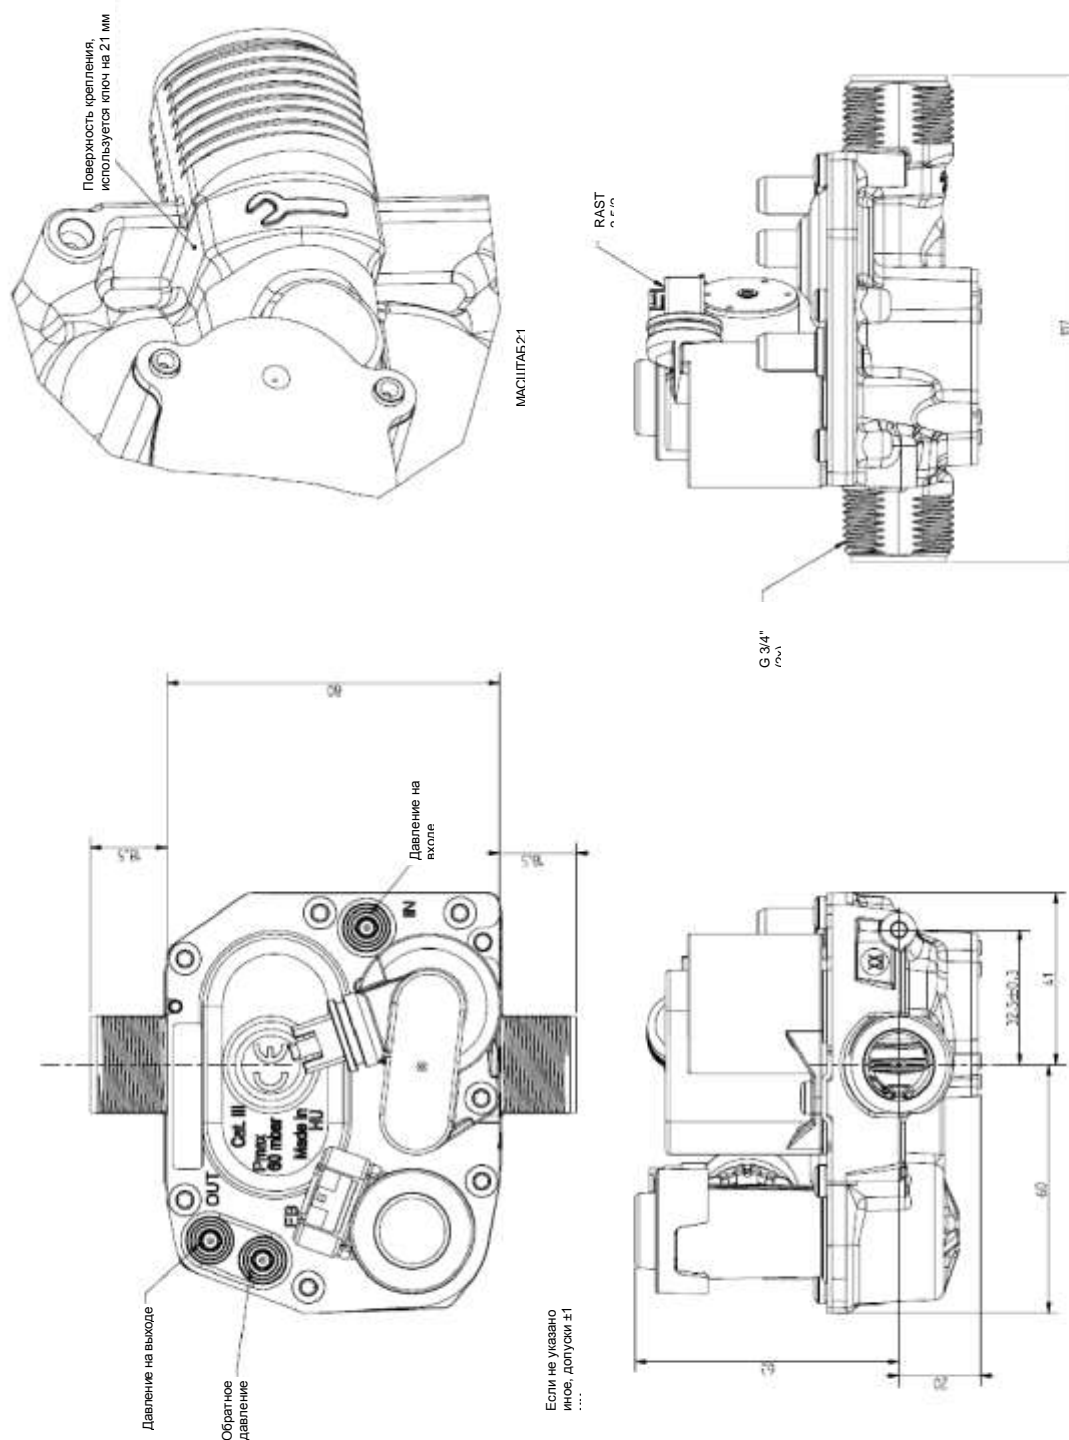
Габаритный чертеж VK4305H/VK8305V
